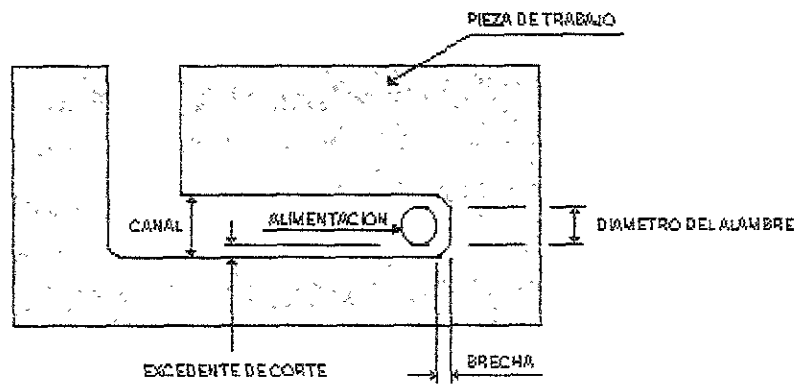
Definición del canal y el excedente en el corte por descarga eléctrica con alambre.
